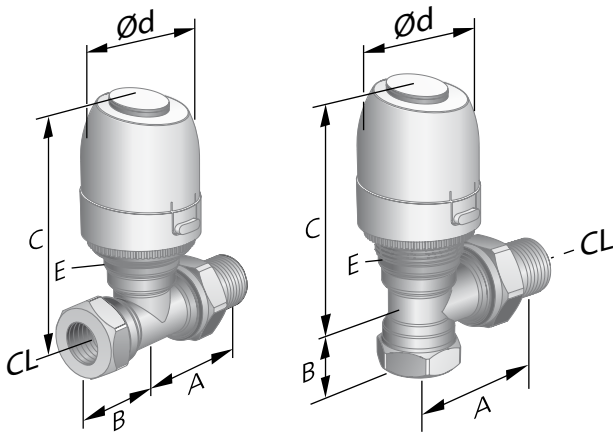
Vanne VALVE-S (version droite) et VALVE-A (version coudée) illustrées avec servomoteur ACTUATOR.
